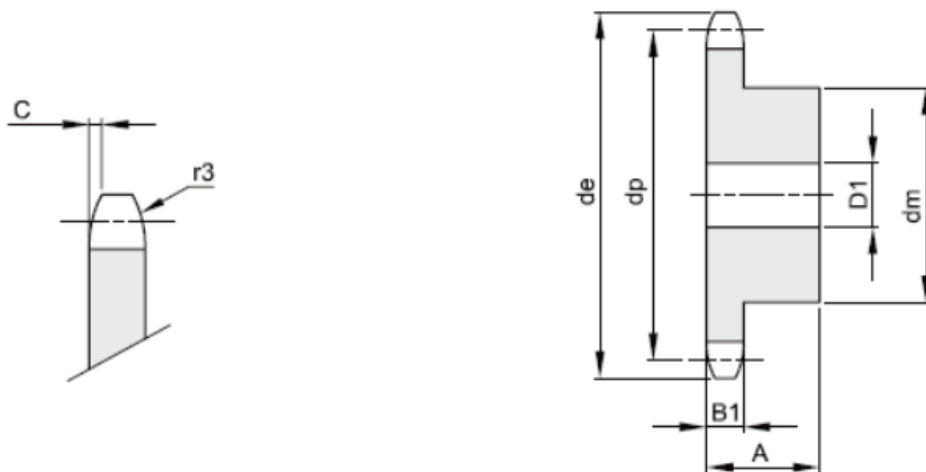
Medidas da engrenagem para corrente simples. Fonte: ATI Brasil
